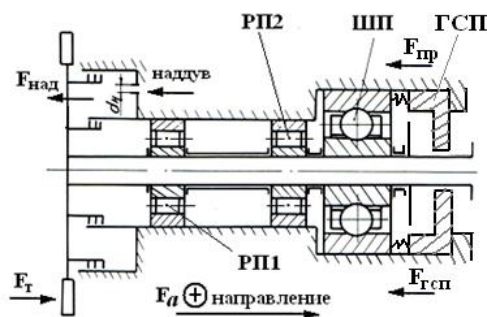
Силевая схема СТ серийного двигателя НК-16СТ с модернизированной задней опорой
